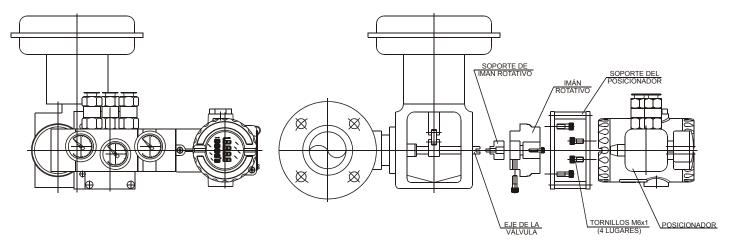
Esquema de montaje del Posicionador en un Actuador Rotativo
